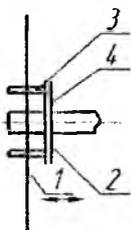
Вариант установки заготовки распиловочного диска с использованием штифтов
